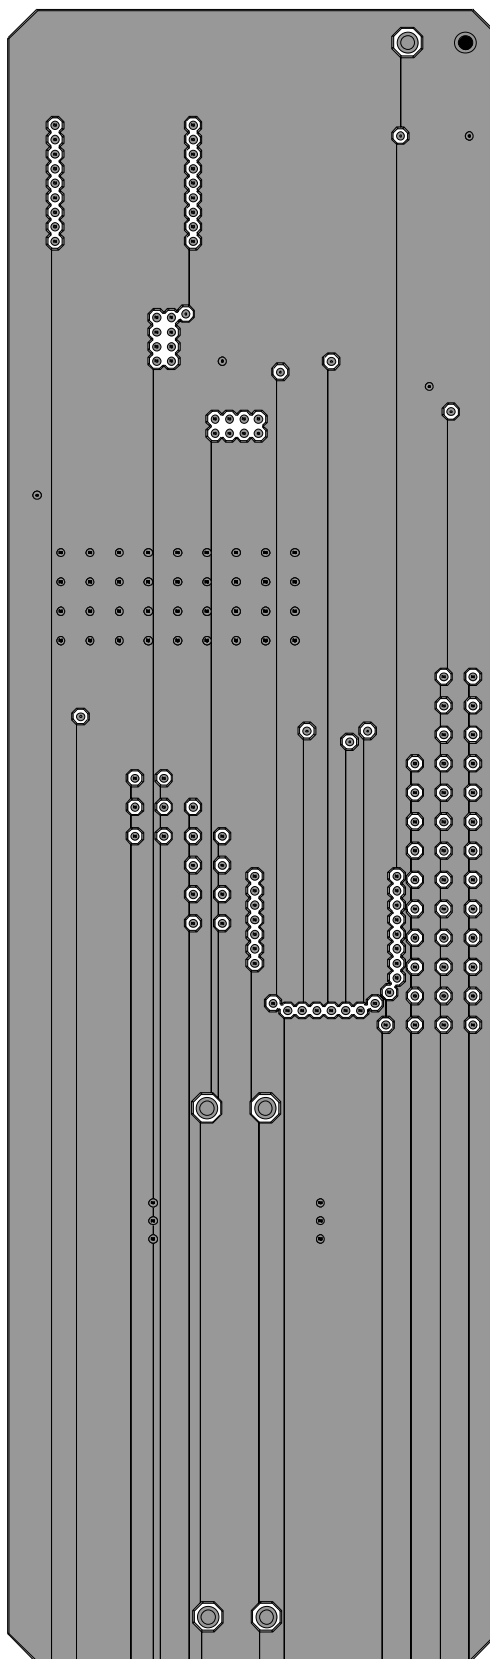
+3,3V-omvandlare lager 2 helt jordplan
